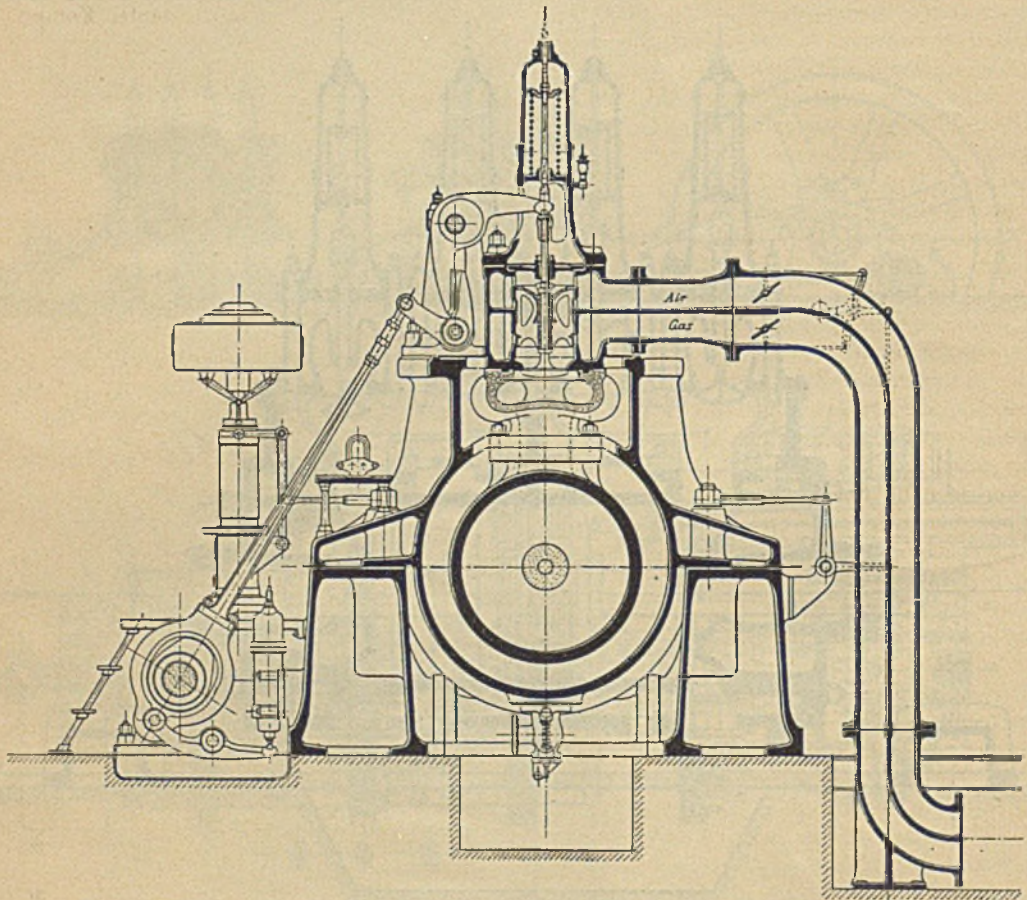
Steuerung zum Gasmotor von Fried. Krupp, Akt.-Ges.
